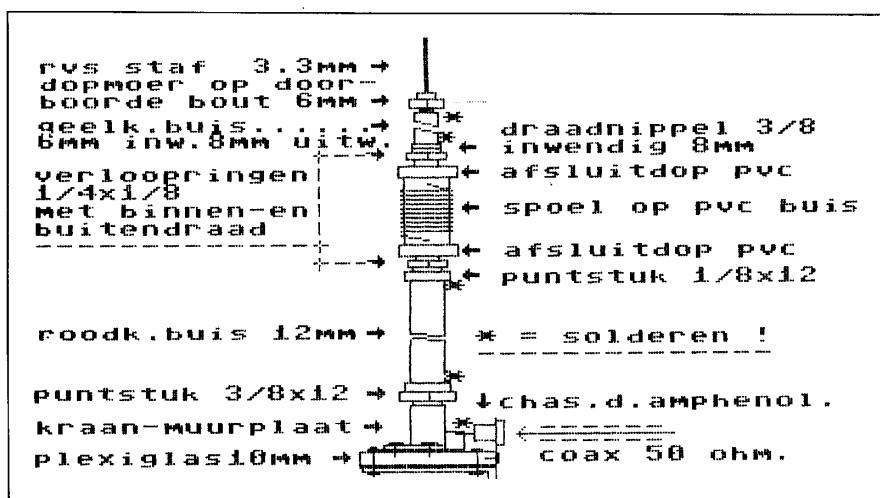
Naam, plaats en overzicht van de onderdelen.
